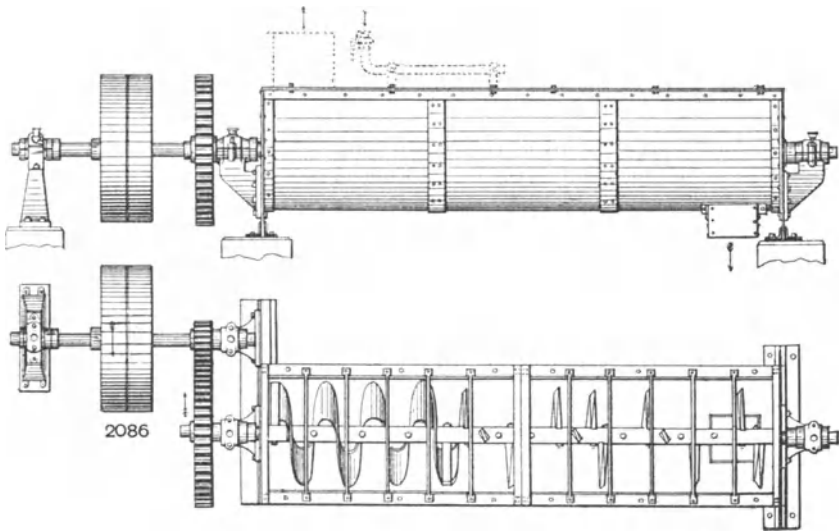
Misch- und Bewässerungsschnecke (G. Luther AG., Braunschweig).
